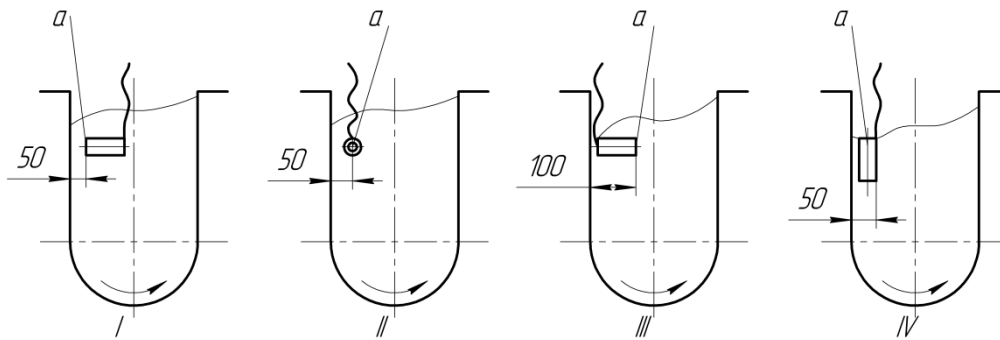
Схема расположения датчика-детали в резервуаре вибростанка:
